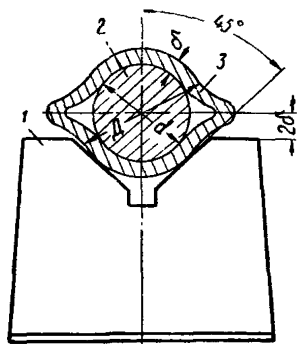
Конструкция электрода для контактной стыковой сварки элементов арматуры с гильзами
